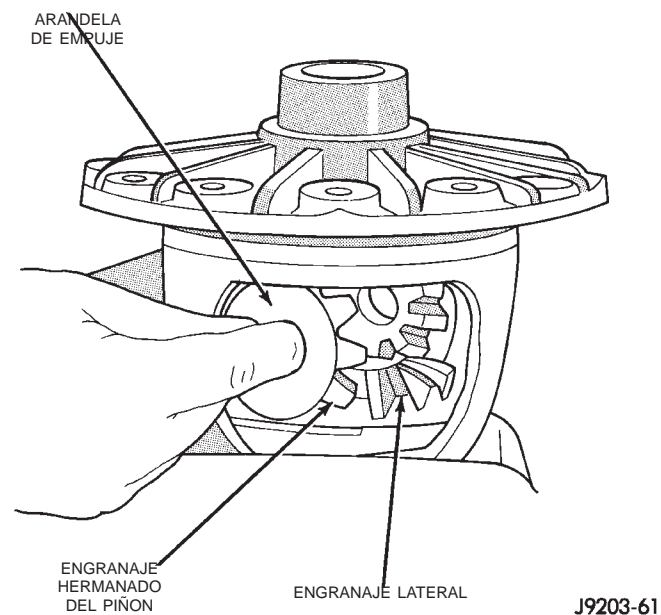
Desmontaje de los engranajes hermanados del piñón
